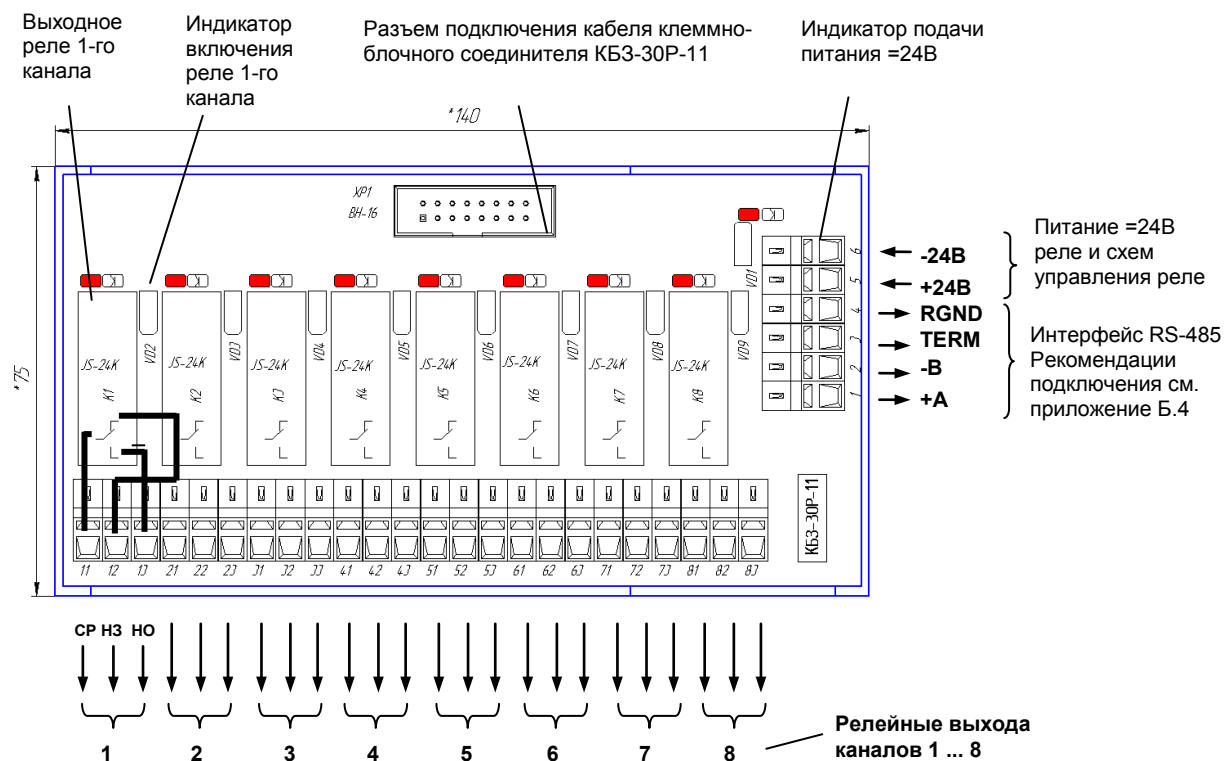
расположение сигналов и габаритные размеры клеммно-блочного соединителя КБЗ-30Р-11
